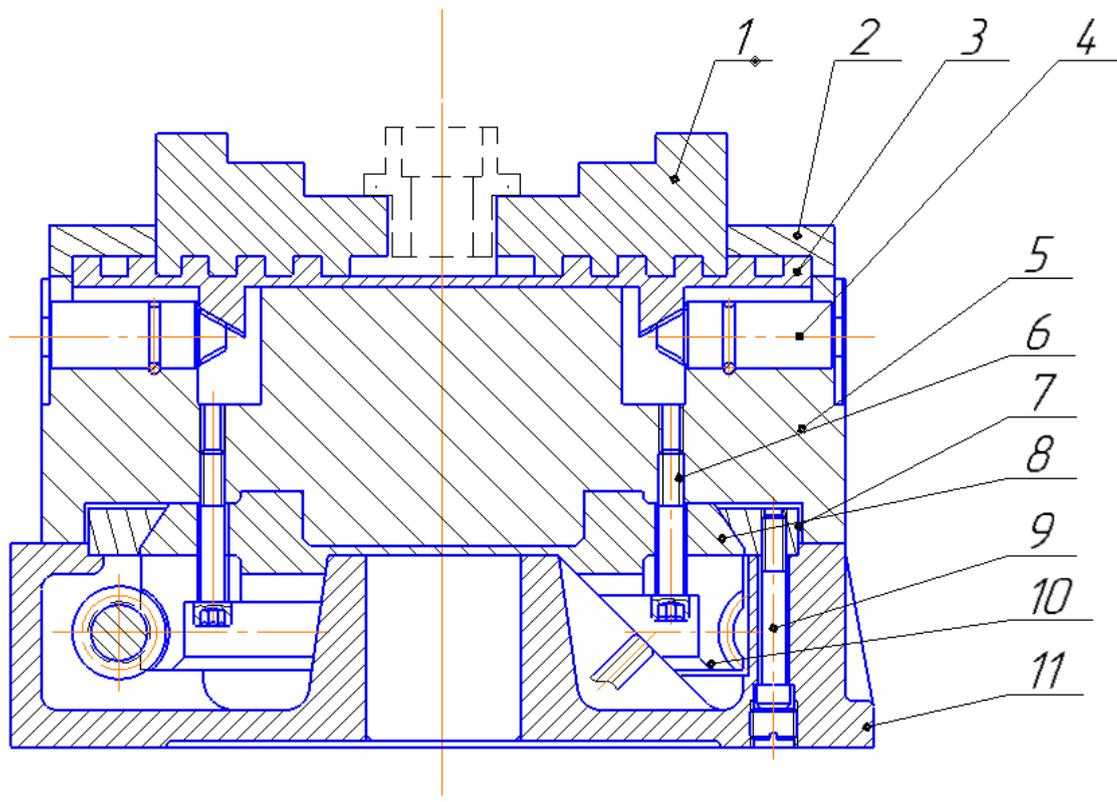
Компоновка (общий вид) приспособления показан на чертеже.
